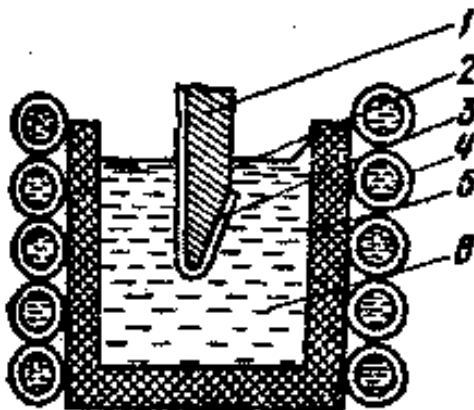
Схема індукційного наплавлення рідким присадним металом:
